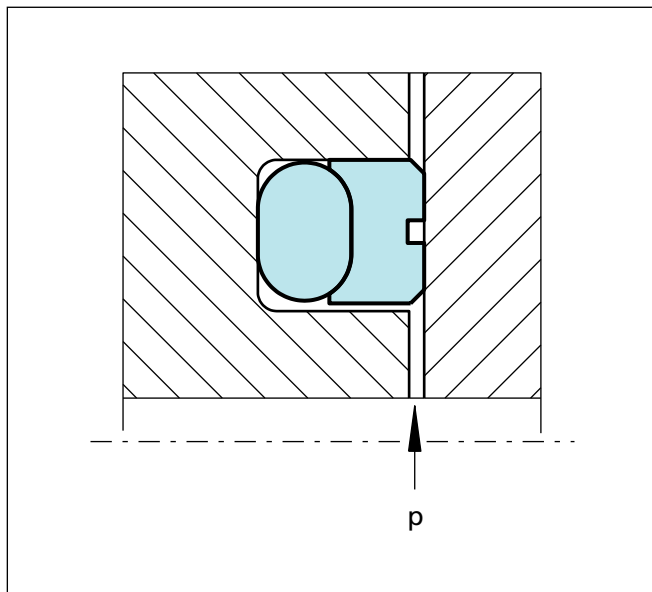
Axialwirkender Turcon® Roto Glyd Ring®
